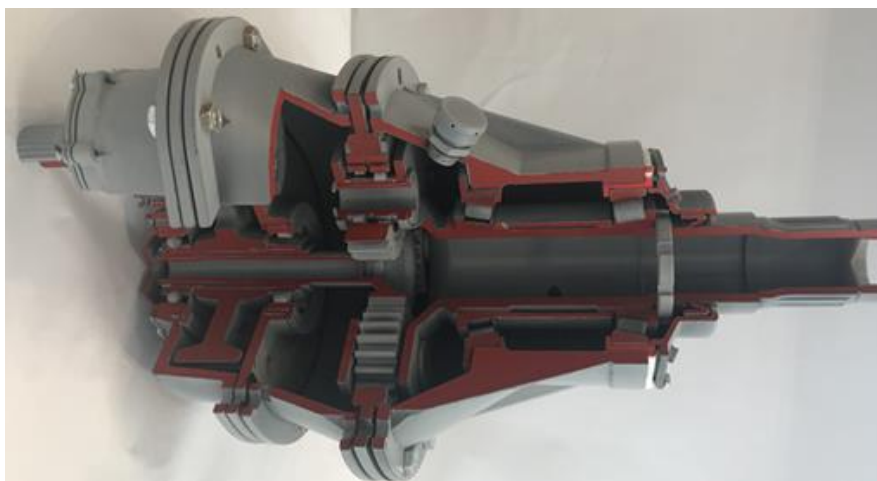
Макет наглядного пособия "Редуктор вертолѐта" в сборе
